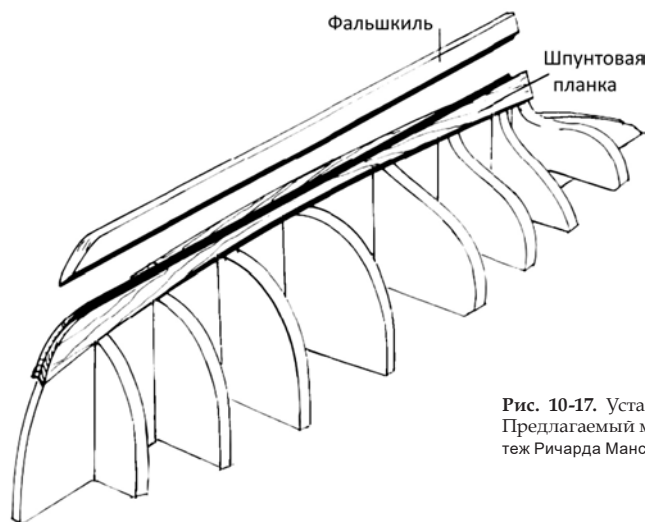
Установка шпунтовой планки. Предлагаемый метод начала обшивки (Чертеж Ричарда Мансира).
